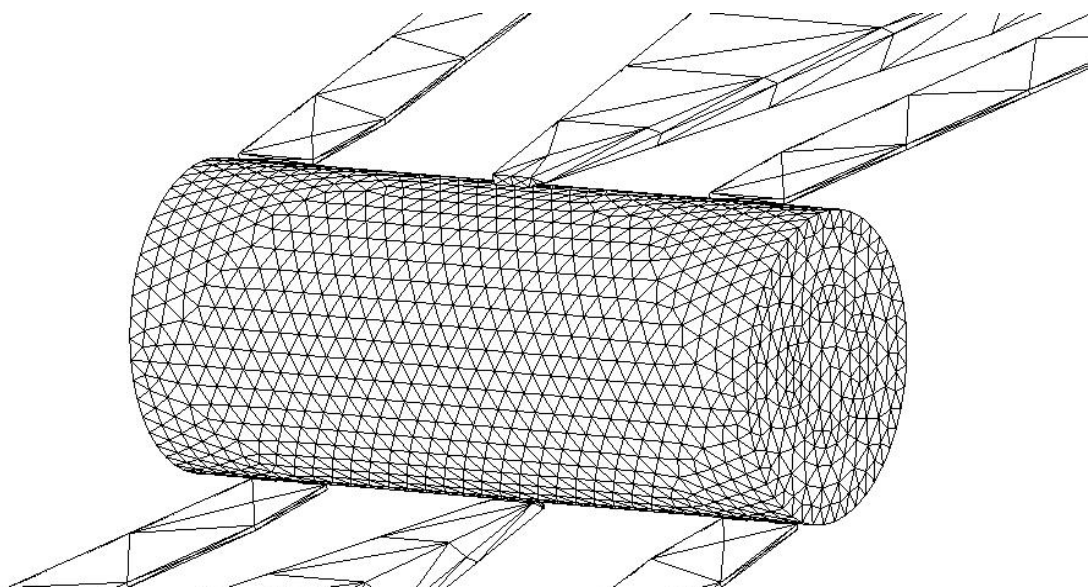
Конечно-элементная модель заготовки (начальная форма)
